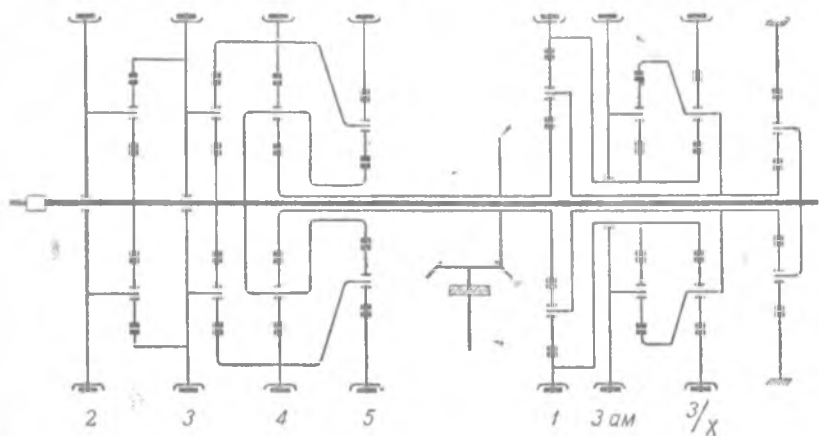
Кинематическая схема эпициклической коробки перемены передач типа „Вильсон“ танка МК-IIа
